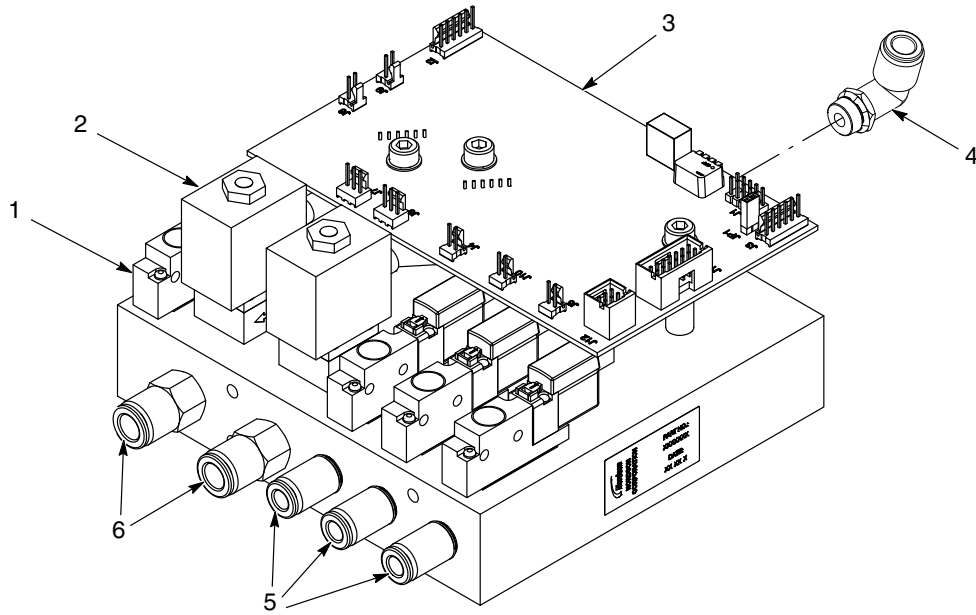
Panel Montaj Grubu Parçaları (3 / 3)
